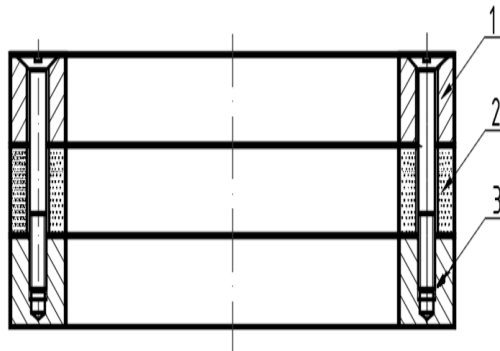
Схема конструкції кришки кокілю: 1 – Кришки із сплаву титана; 2 – пористий ізолятор; 3 – штифтовий з'єднувальний вузол
